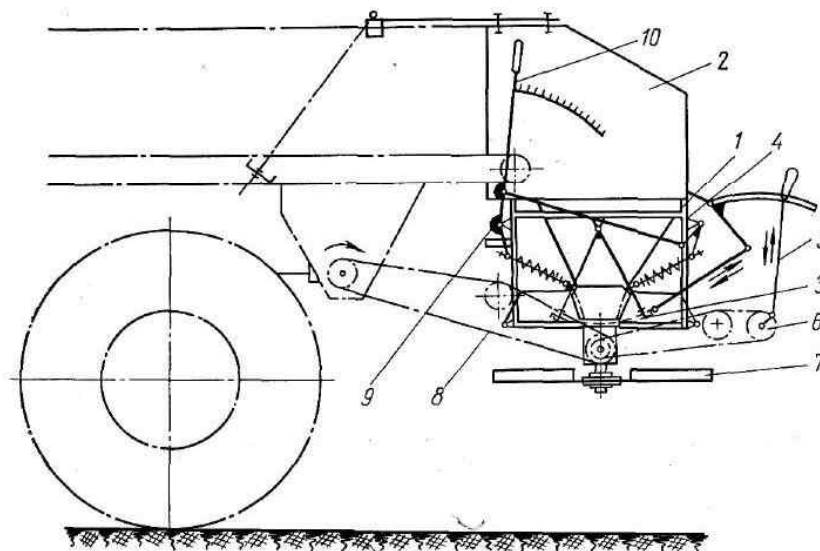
Схема разбрасывателя удобрений и извести РМИ-2.
